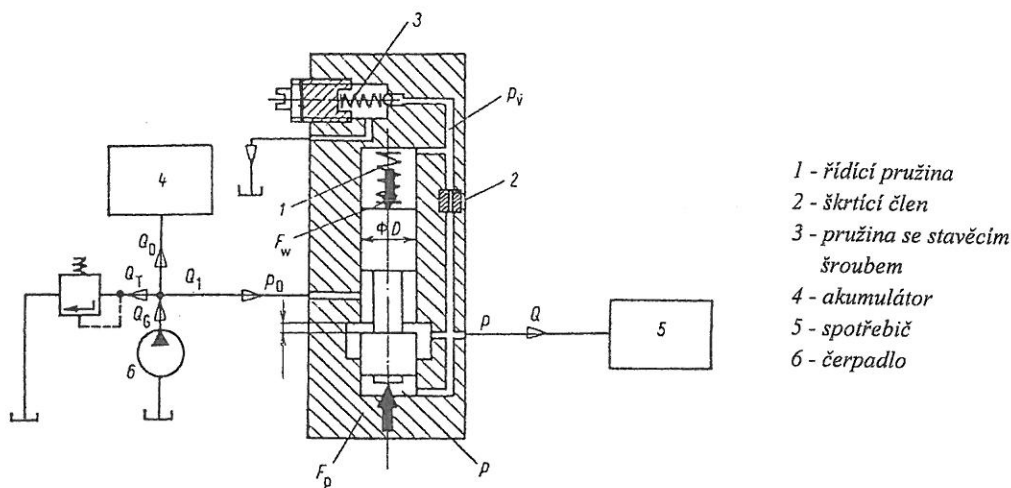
Konstrukční uspořádání tlakových ventilů
